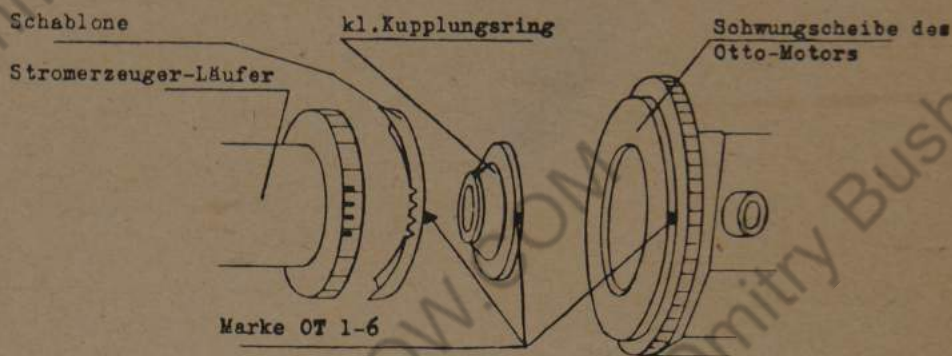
Einstellmarkierung zum Anflanschen des Stromerzeugers an dem Otto-Motor
